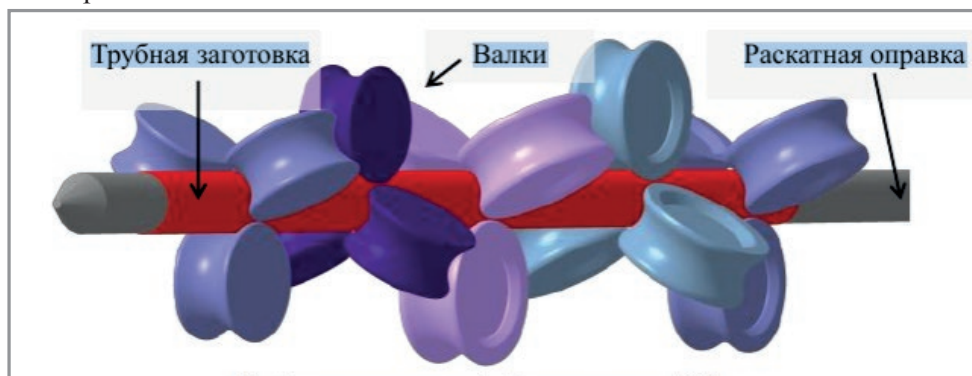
Схема раскатки трубной заготовки в стане PQF
